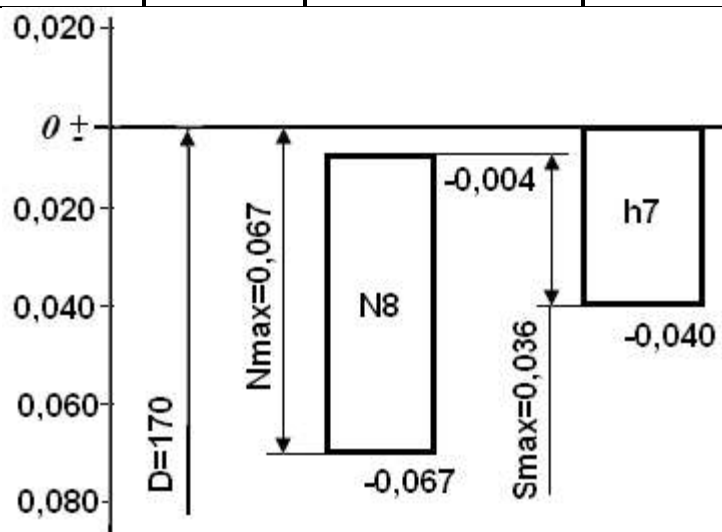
Схема розташування полів допусків деталей з'єднання Ø170N8/h7
